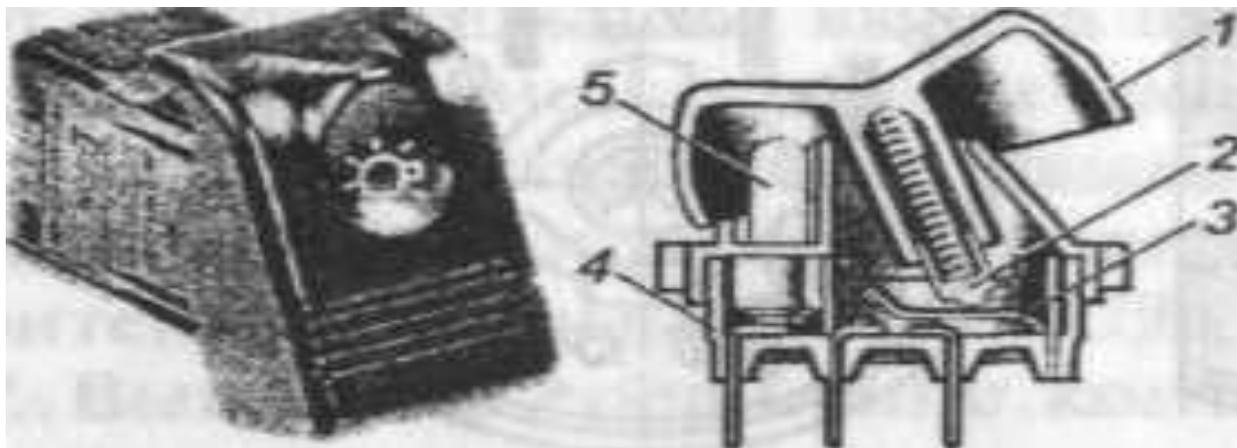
Клавишный выключатель 84.3709 (а) и его конструкция (б): 1 — клавиша; 2 — толкатель; 3 — контактная пластина; 4 — корпус; 5 — лампа подсветки.
